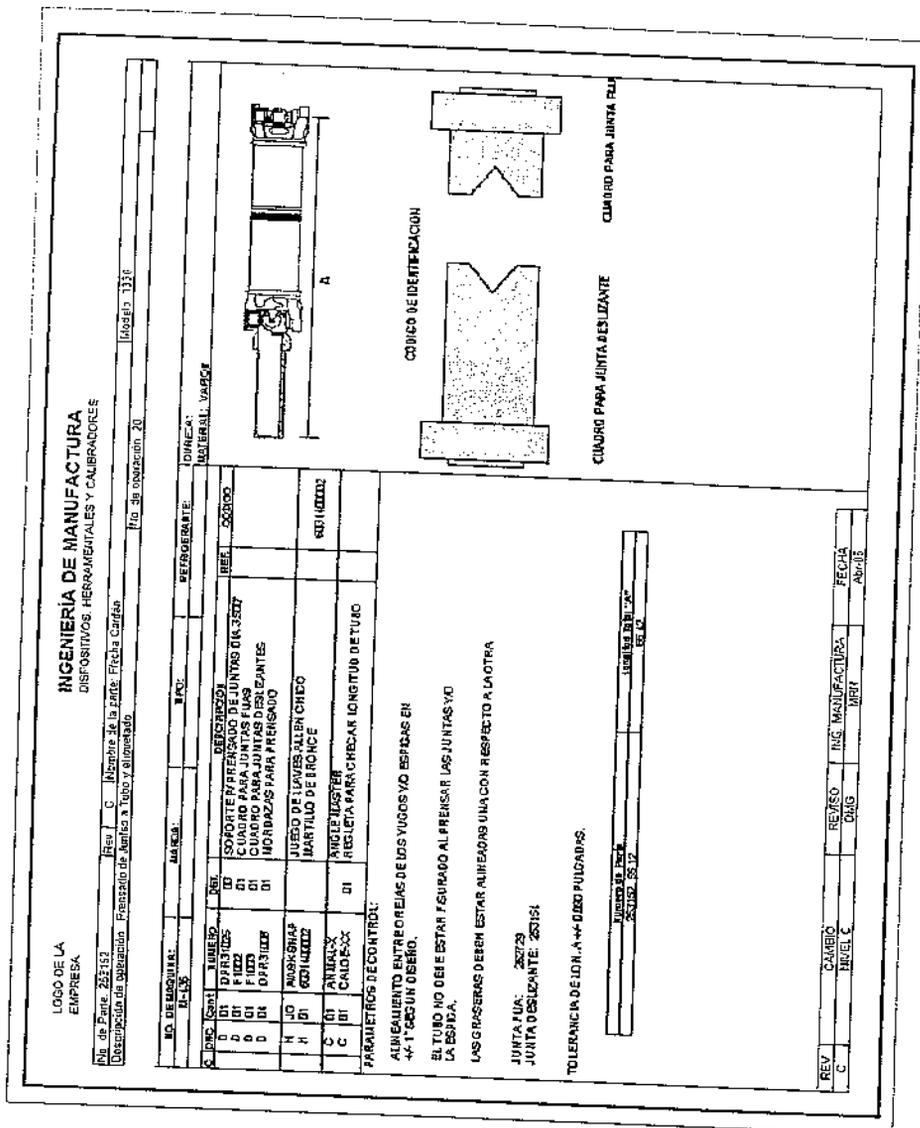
Prensa de Juntas a Tubo y etiquetado
